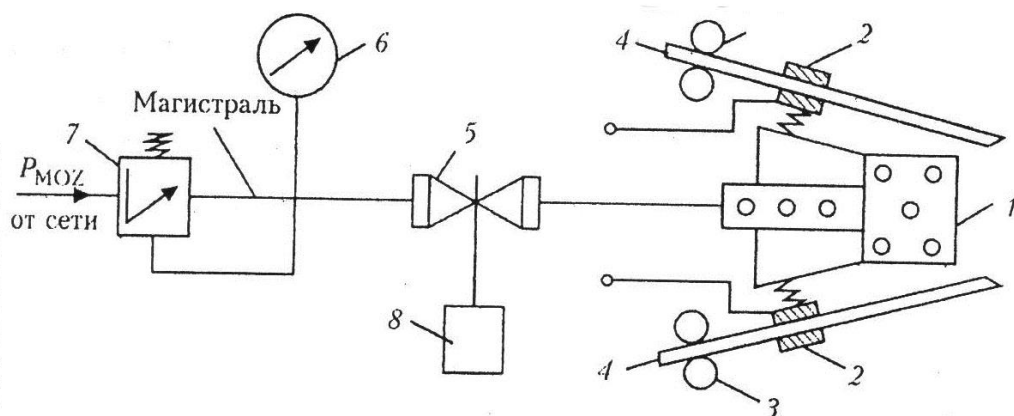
Схема головки металлизатора для пульсирующего распыления:
